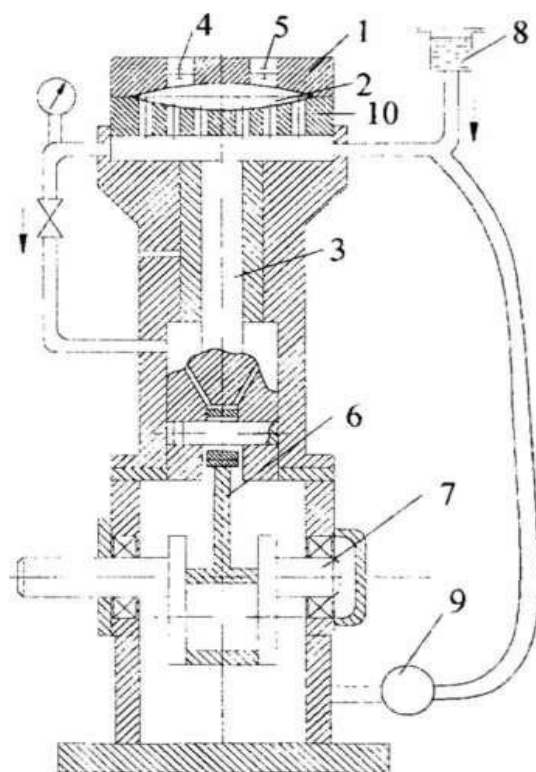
Мембранный компрессор с гидравлическим приводом мембраны: 1 - крышка; 2 - мембрана; 3 - поршень; 4 - всасывающий клапан; 5 - нагнетательный клапан; 6 - шатун; 7 - вал; 8 - емкость; 9 - дозировочный насос; 10 - опорная плита
